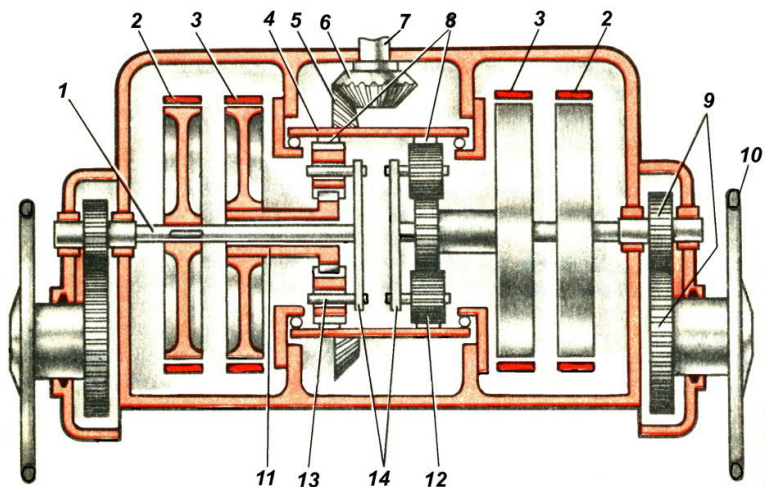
Схема заднего моста гусеничного трактора с планетарными механизмами поворота:
